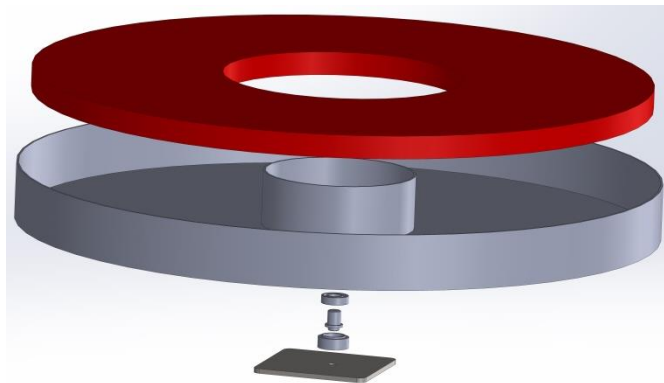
Sistema suporte rolo perfil 023 – vista explodida
